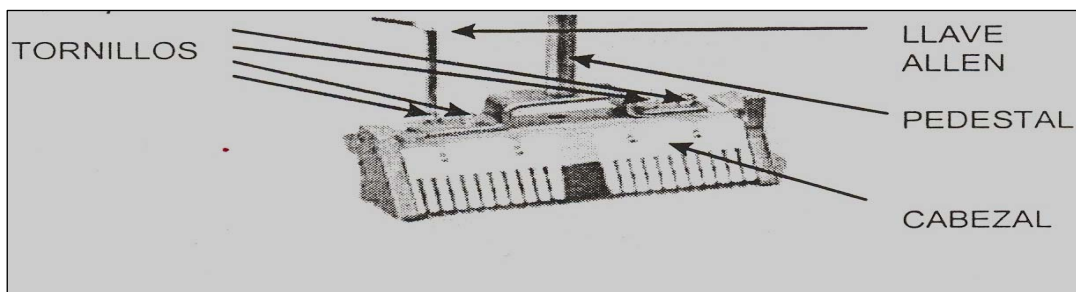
Ensamble del Cabezal y el Pedestal.
